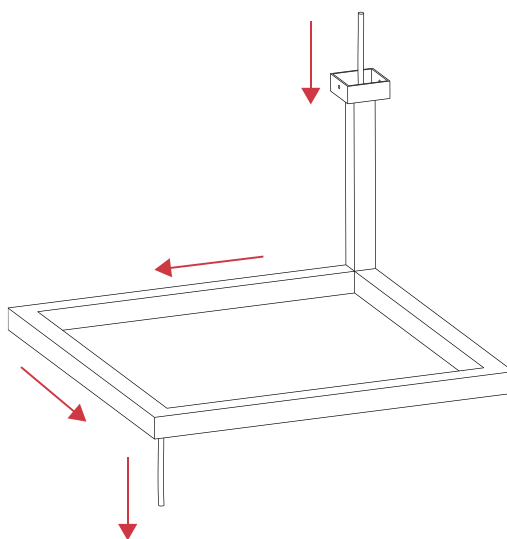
Instalación del cableado por el interior de la estructura de la lámpara de techo.
